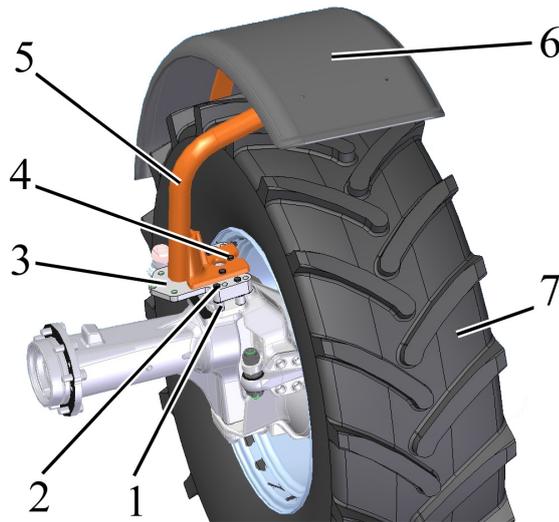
Смазка подшипников осей шкворней ПВМ
